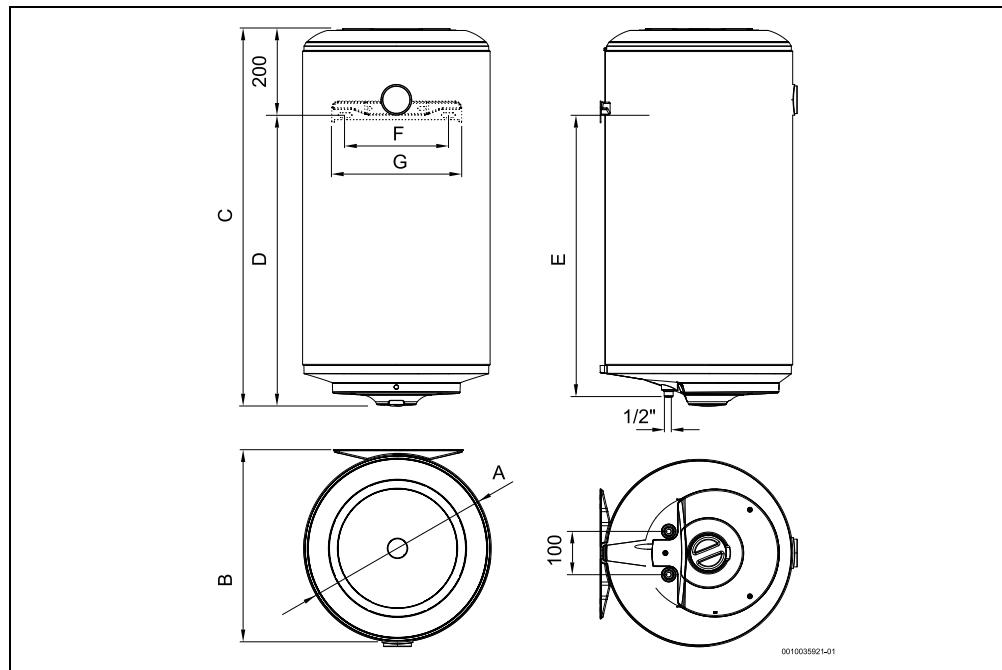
Размеры в мм (монтаж на стене, вертикальный монтаж)
